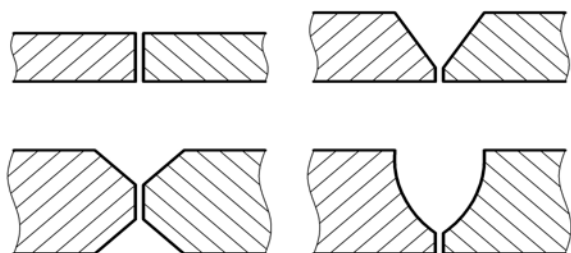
Формы кромок деталей, подготовленных к сварке
